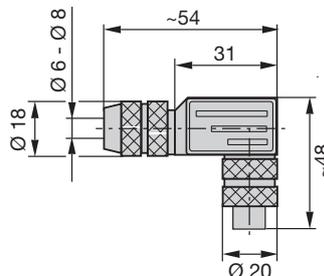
Connettore BKS-S106-00 (spina) per BUS OUT
